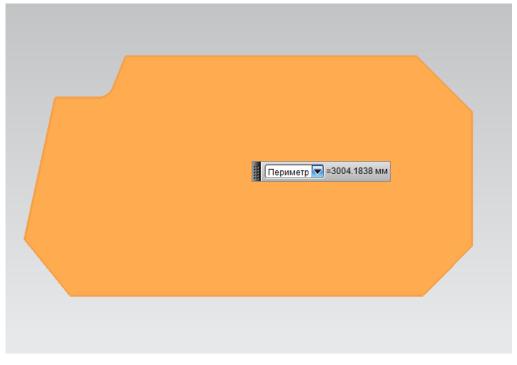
Периметр предлагаемой вырубаемой заготовки
